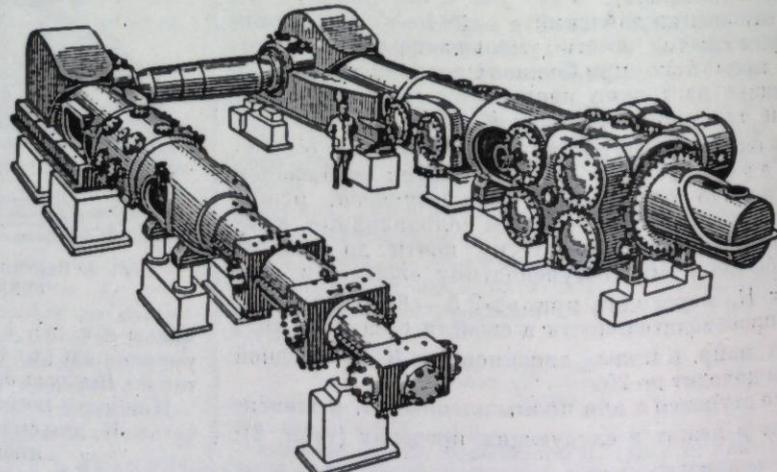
Многоступенчатый поршневой горизонтальный компрессор.
